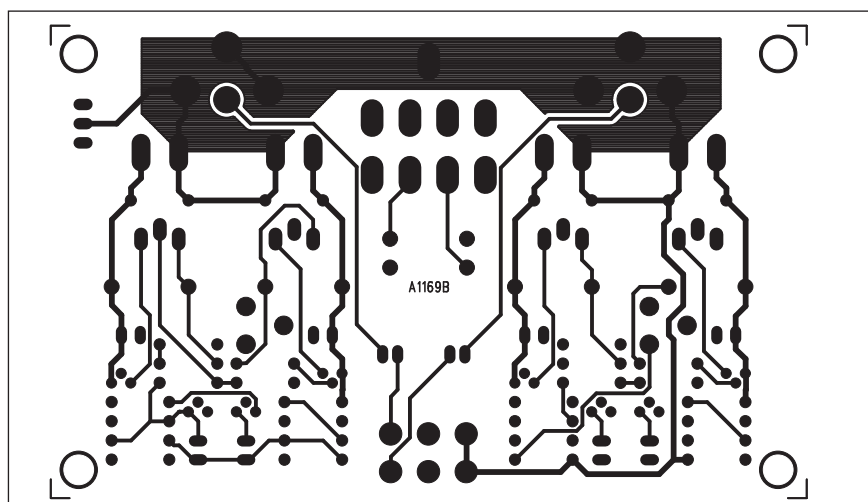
Obrazec desky spojů stereofonního zesilovače (strana BOTTOM)
